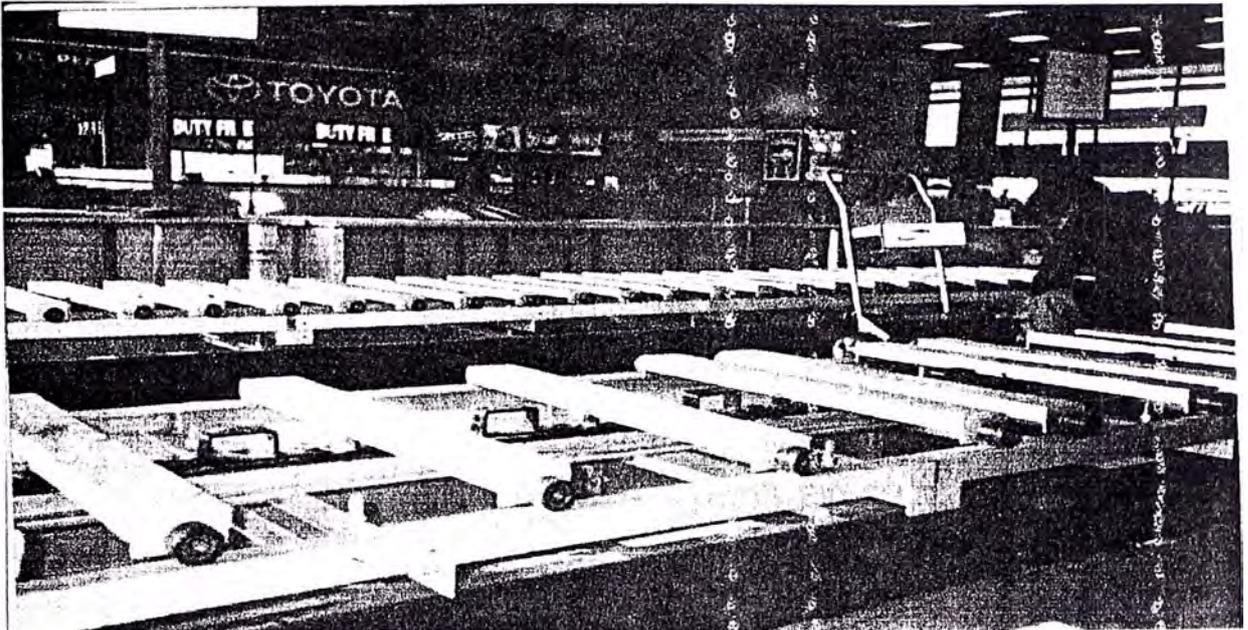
FABRICACION Y MONTAJE DE UNA FAJA TRANSPORTADORA DE EQUIPAJES - JORGE CHAVEZ
